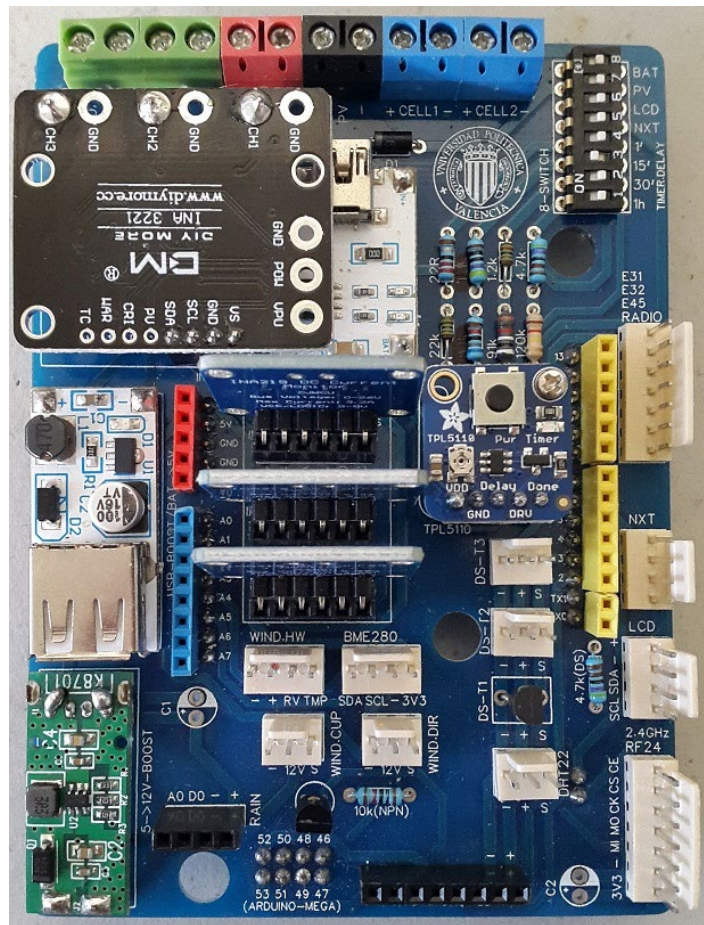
Placa de circuito impreso del transmisor soldada.
